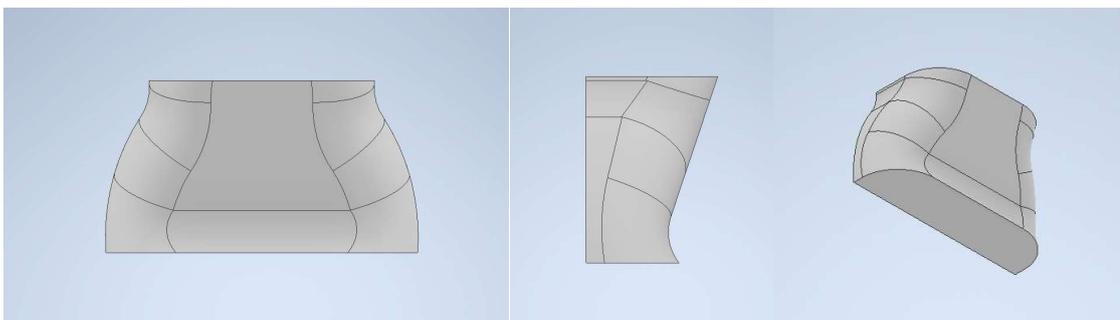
Alzado, perfil y vista en perspectiva de la espalda.
